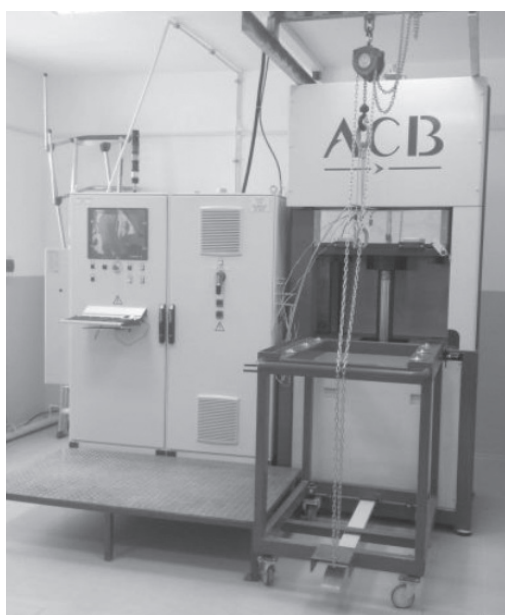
Пресс сверхпластической формовки и диффузионной сварки FSP60T
